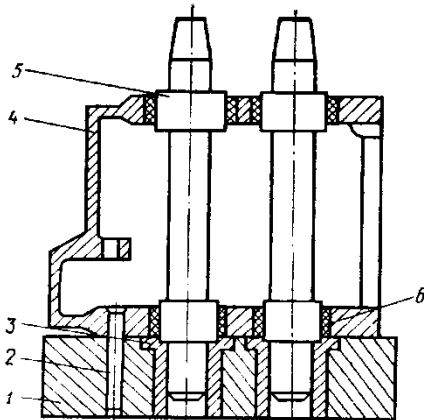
Схема формування посадочних місць вальниць корпусу коробки передач:
